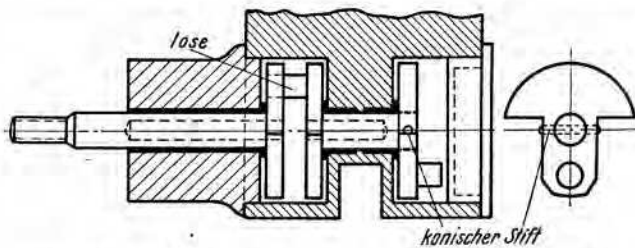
Aufbau der Kurbelwelle beim Zweizylindermotor
